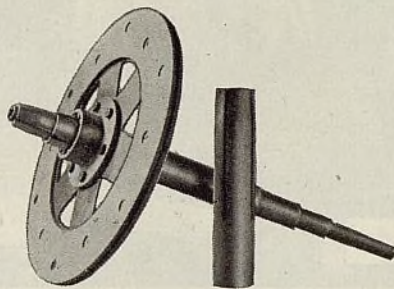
Una herramienta para alinear exactamente el embrague al momento de instalarlo
